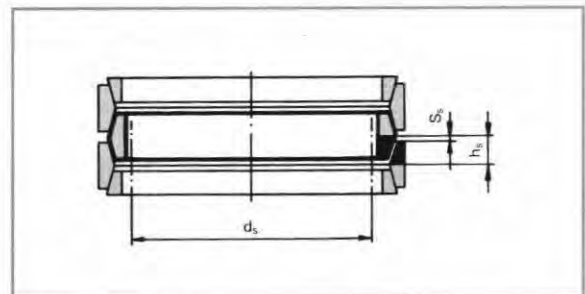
Beim Einbau geschlitzter Innenringe ausnutzbaren Innendurchmesser d_s beachten.
